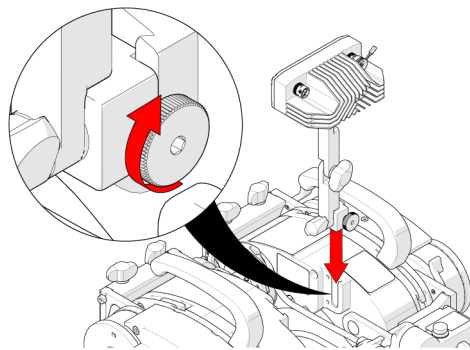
Fixer la caméra et serrer la vis à ailettes
